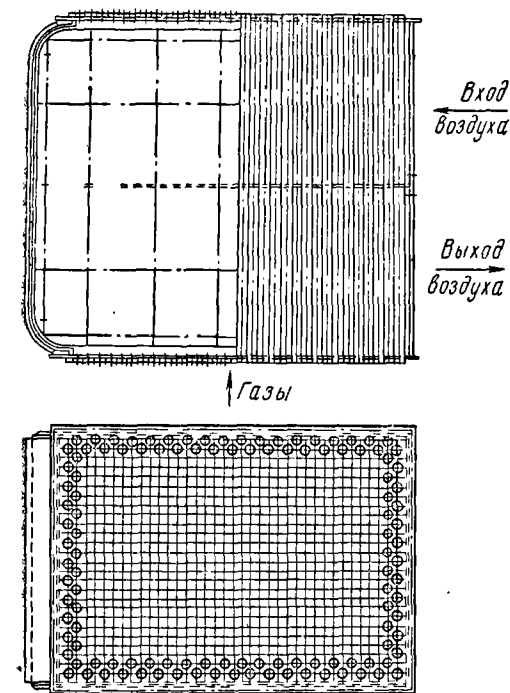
Вертикальный двухпроточный гладкотрубный воздухоподогреватель
